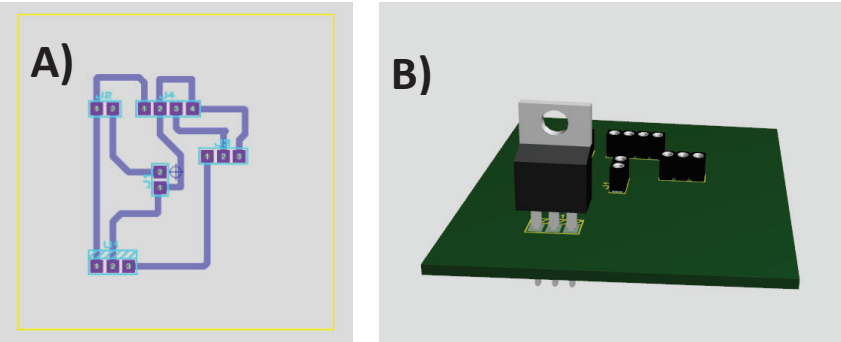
A) Diseño del circuito impreso (PCB), B) Vista 3d del diseño.
